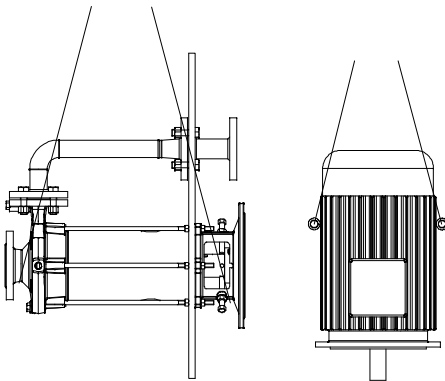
Как вариант - транспортировка насоса / двигателя типоразмеров, начиная с 180 при больших глубинах установки ET
